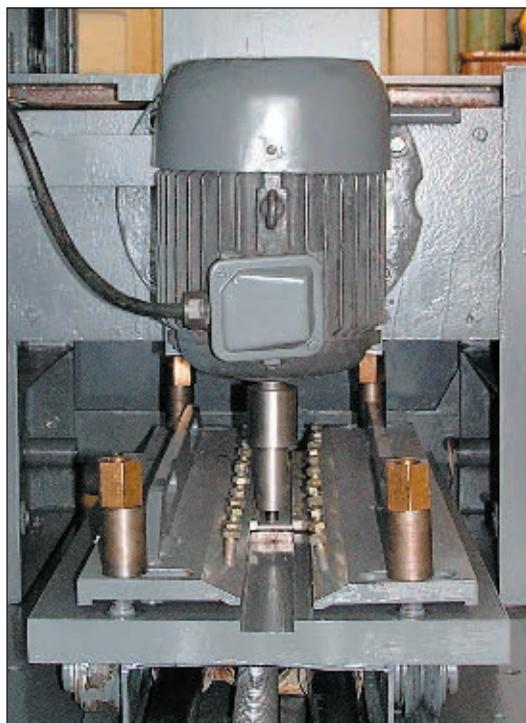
Лабораторная установка для сварки трением с перемешиванием тонколистовых (1,8–2,5 мм) алюминиевых сплавов
